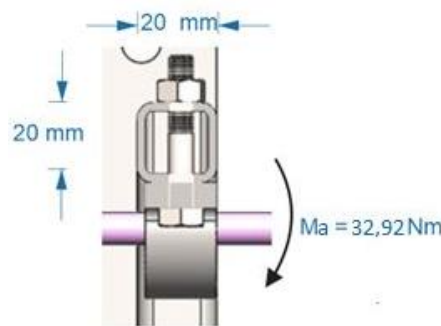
Vista de corte en estructura de apoyo - Mecanismo de leva radial.
